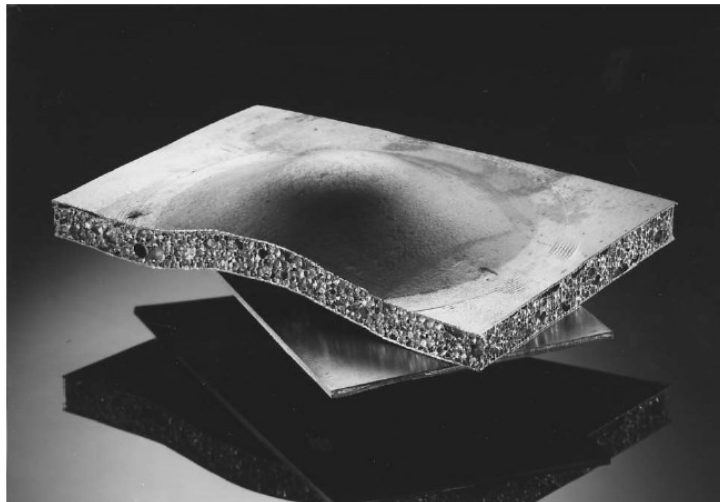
Estructura tipo "Sandwich" hecha con una espuma metálica de aluminio. (Banhart, John. 2000)
